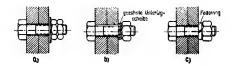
Schraubensicherung durch Gegenmutter (a), gezahnte Unterlegscheibe (b) ader Federring (c)
